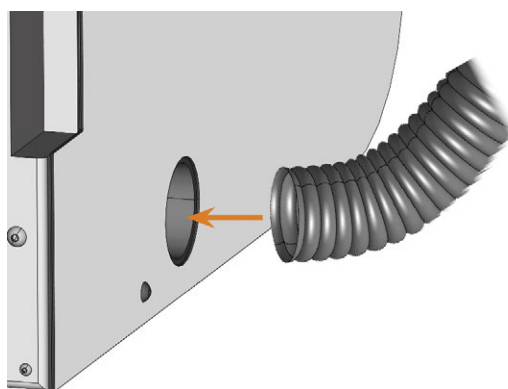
INSERIMENTO DEL TUBO DI ASPIRAZIONE NELLA MACCHINA
